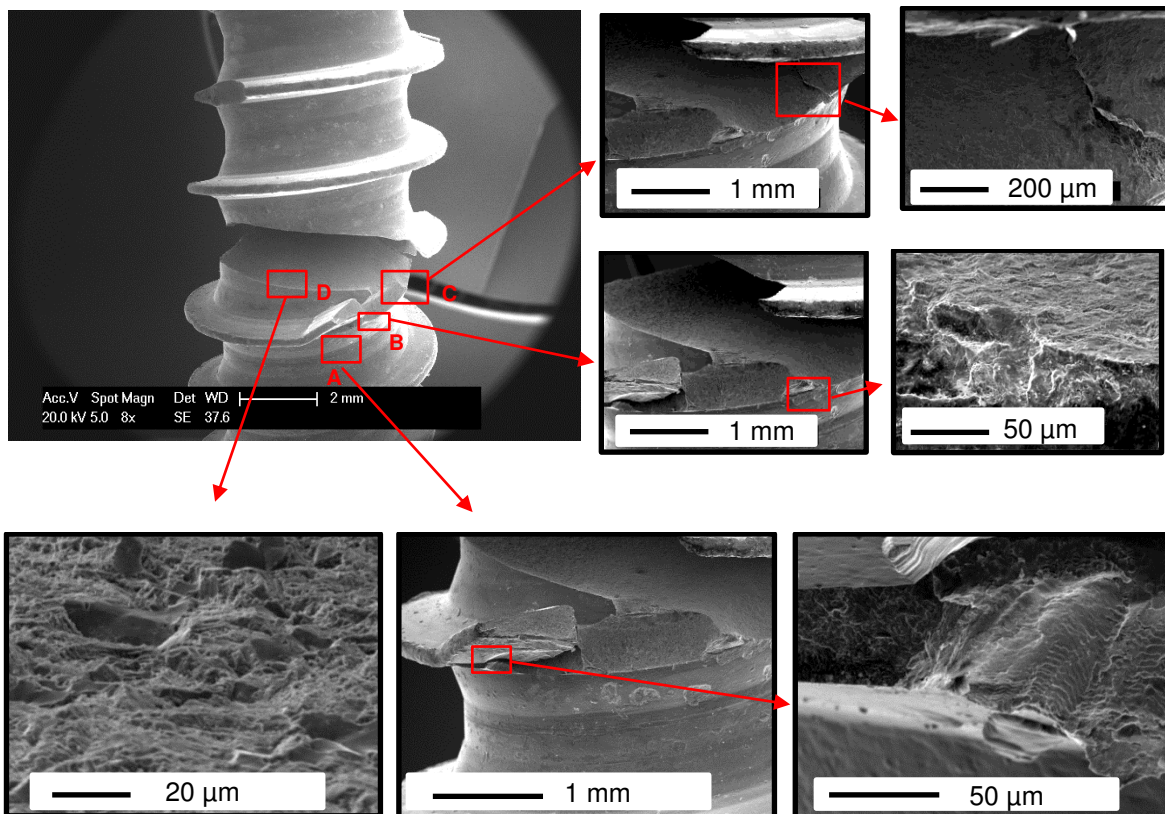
REM-Aufnahmen einer ideal ausgewalzten Schraube nach ca. 3,8 Millionen Zyklen
